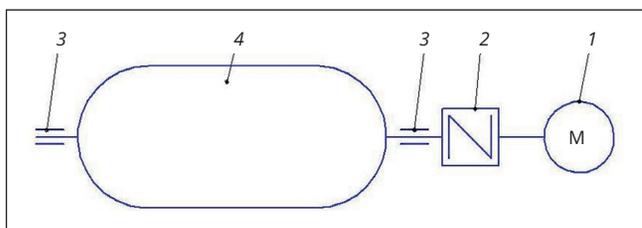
Кинематическая схема привода вращения автоклава после модернизации: 1 – мотор-редуктор; 2 – зубчатая муфта; 3 – подшипниковые узлы; 4 – автоклав
